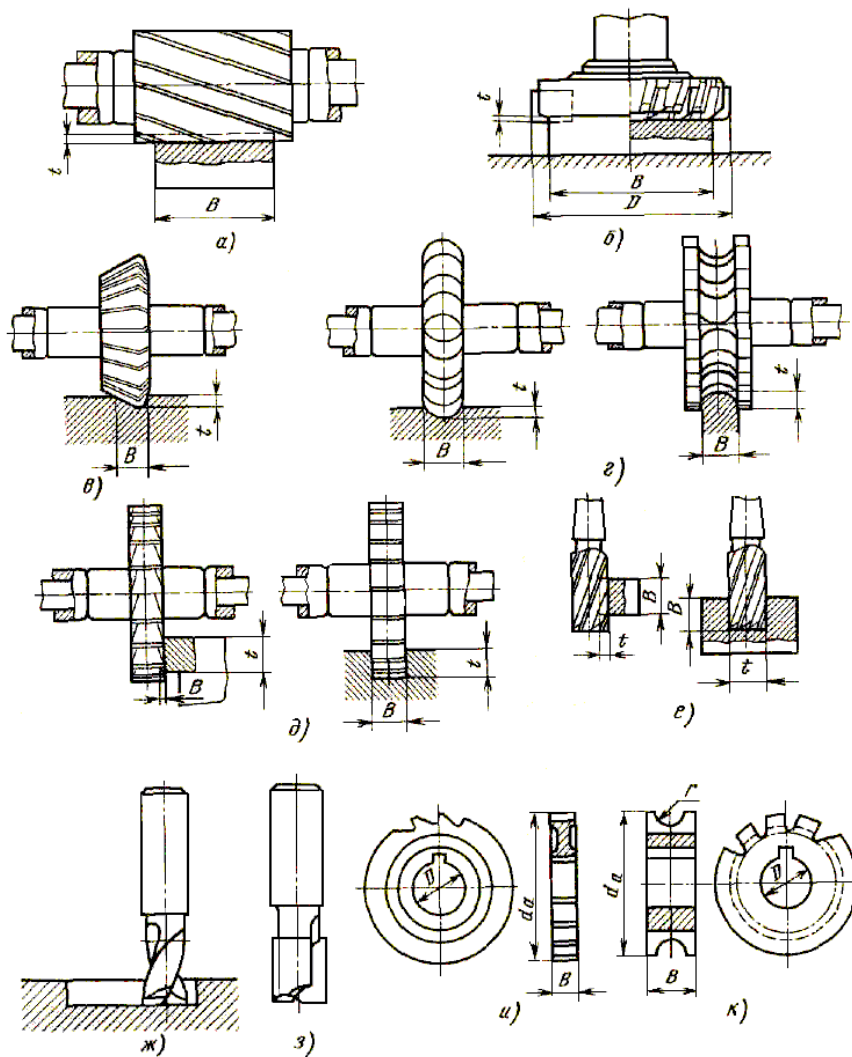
Типы фрез и обрабатываемых поверхностей
